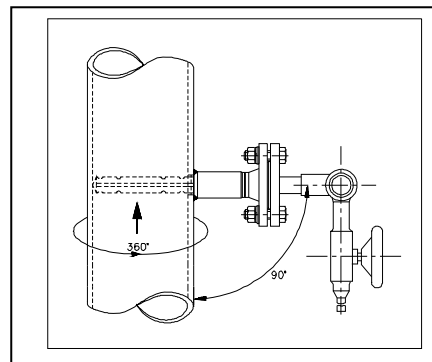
Installation in einer vertikalen Rohrleitung Typ: IBFD-25-K5-A16
